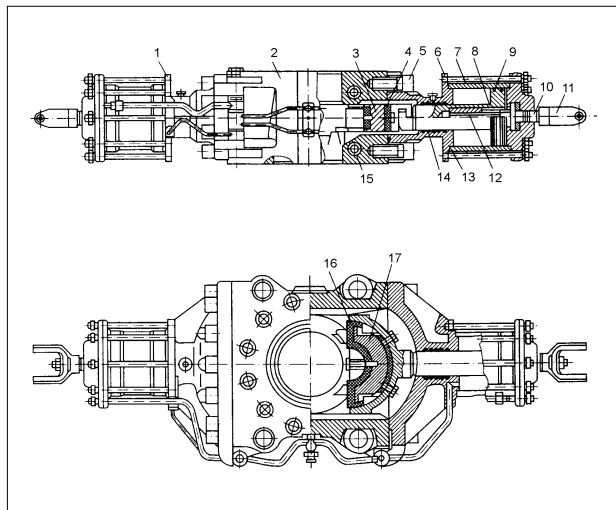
Схема плашкового превентора ППГ: 1, 6 – кришки; 2 – корпус превентора; 3 – корпус плашки; 4 – ущільнення плашки; 5 – гвинти; 7 – гідравлічний циліндр; 8 – поршень; 9, 13, 14 – гумові ущільнюючі кільця; 10 – шліцьовий валік; 11 – вилка; 12 – проміжна різьбова втулка; 15 – паропроводи; 16 – гумовий ущільнювач; 17 – каркас плашки.
